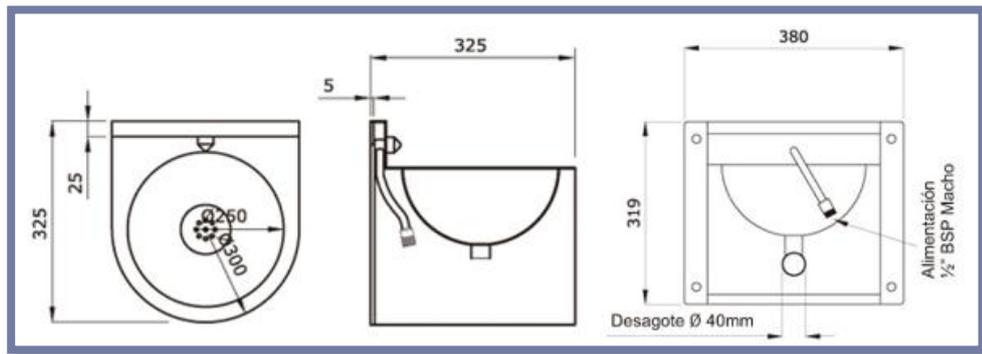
Lavatorio de Manos. Vista en Planta, Corte y Contrafrente, respectivamente.
